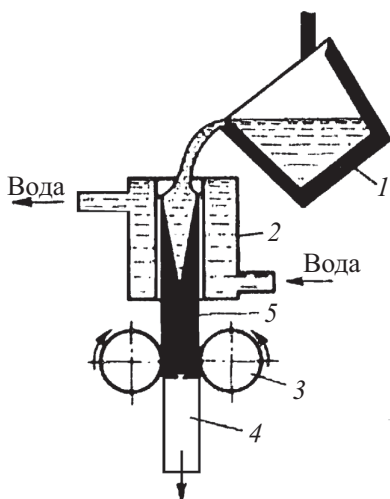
Схема непрерывного вертикального литья заготовок из стали: 1 – ковш с расплавом; 2 – водоохлаждаемый кристаллизатор; 3 – тянущие ролики; 4 – затравка; 5 – вытягиваемая заготовка
